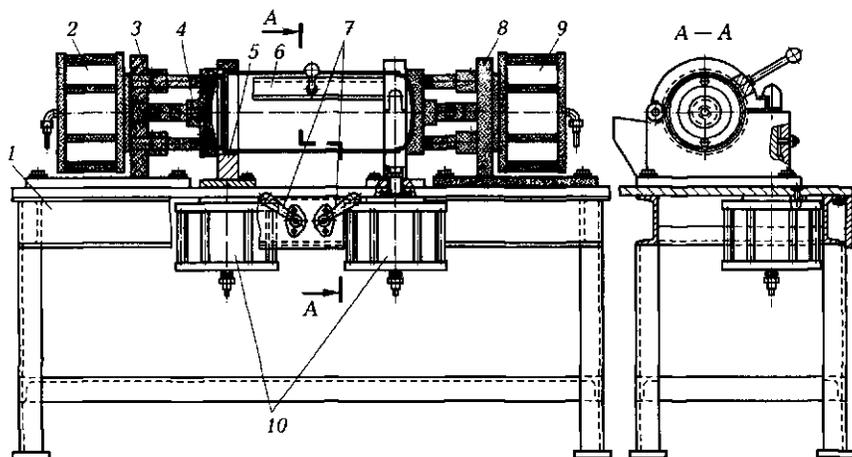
Установка для сборки небольших обечаяек с доньшками:
